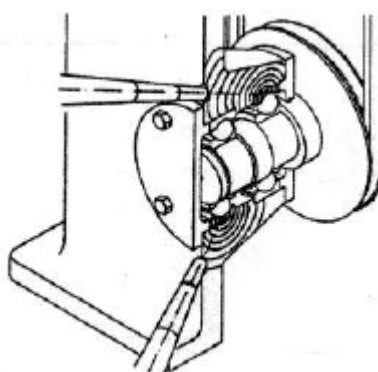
mezi cestou signálu smí být pouze jedno přerušení materiálu [4]
